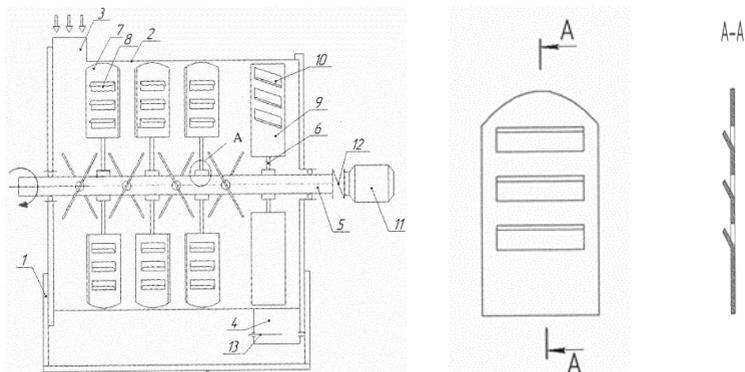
Схема предлагаемого совершенствования вала смесителя:
